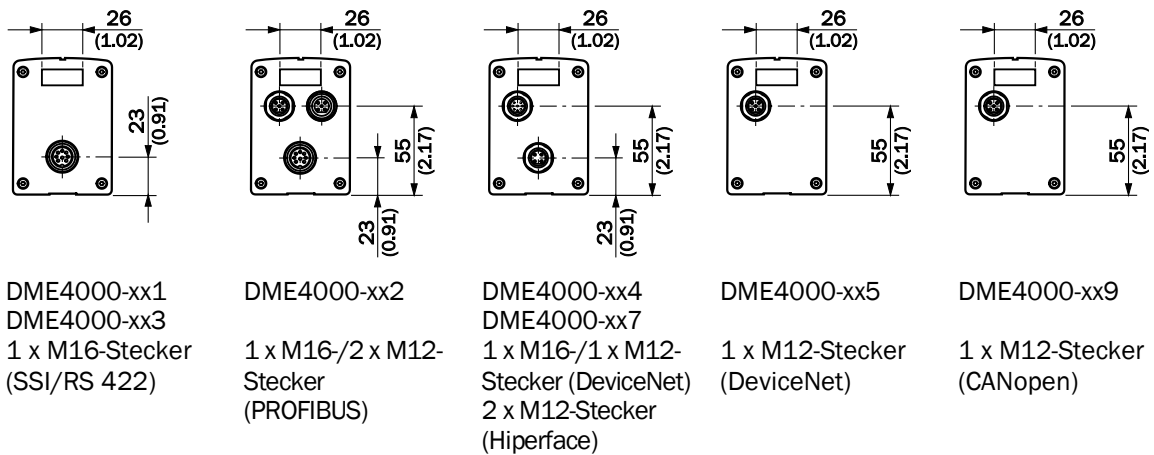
Maßzeichnungen Rückansicht DME4000
